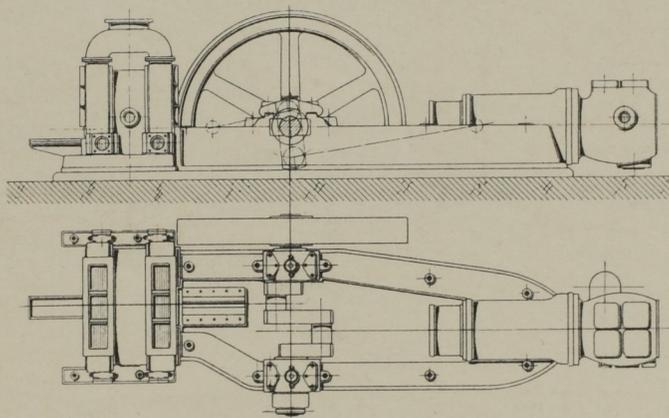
a. Seitenansicht und Grundriss eines gleichwerthigen Gebläses mit Gasmotor-Antrieb.
